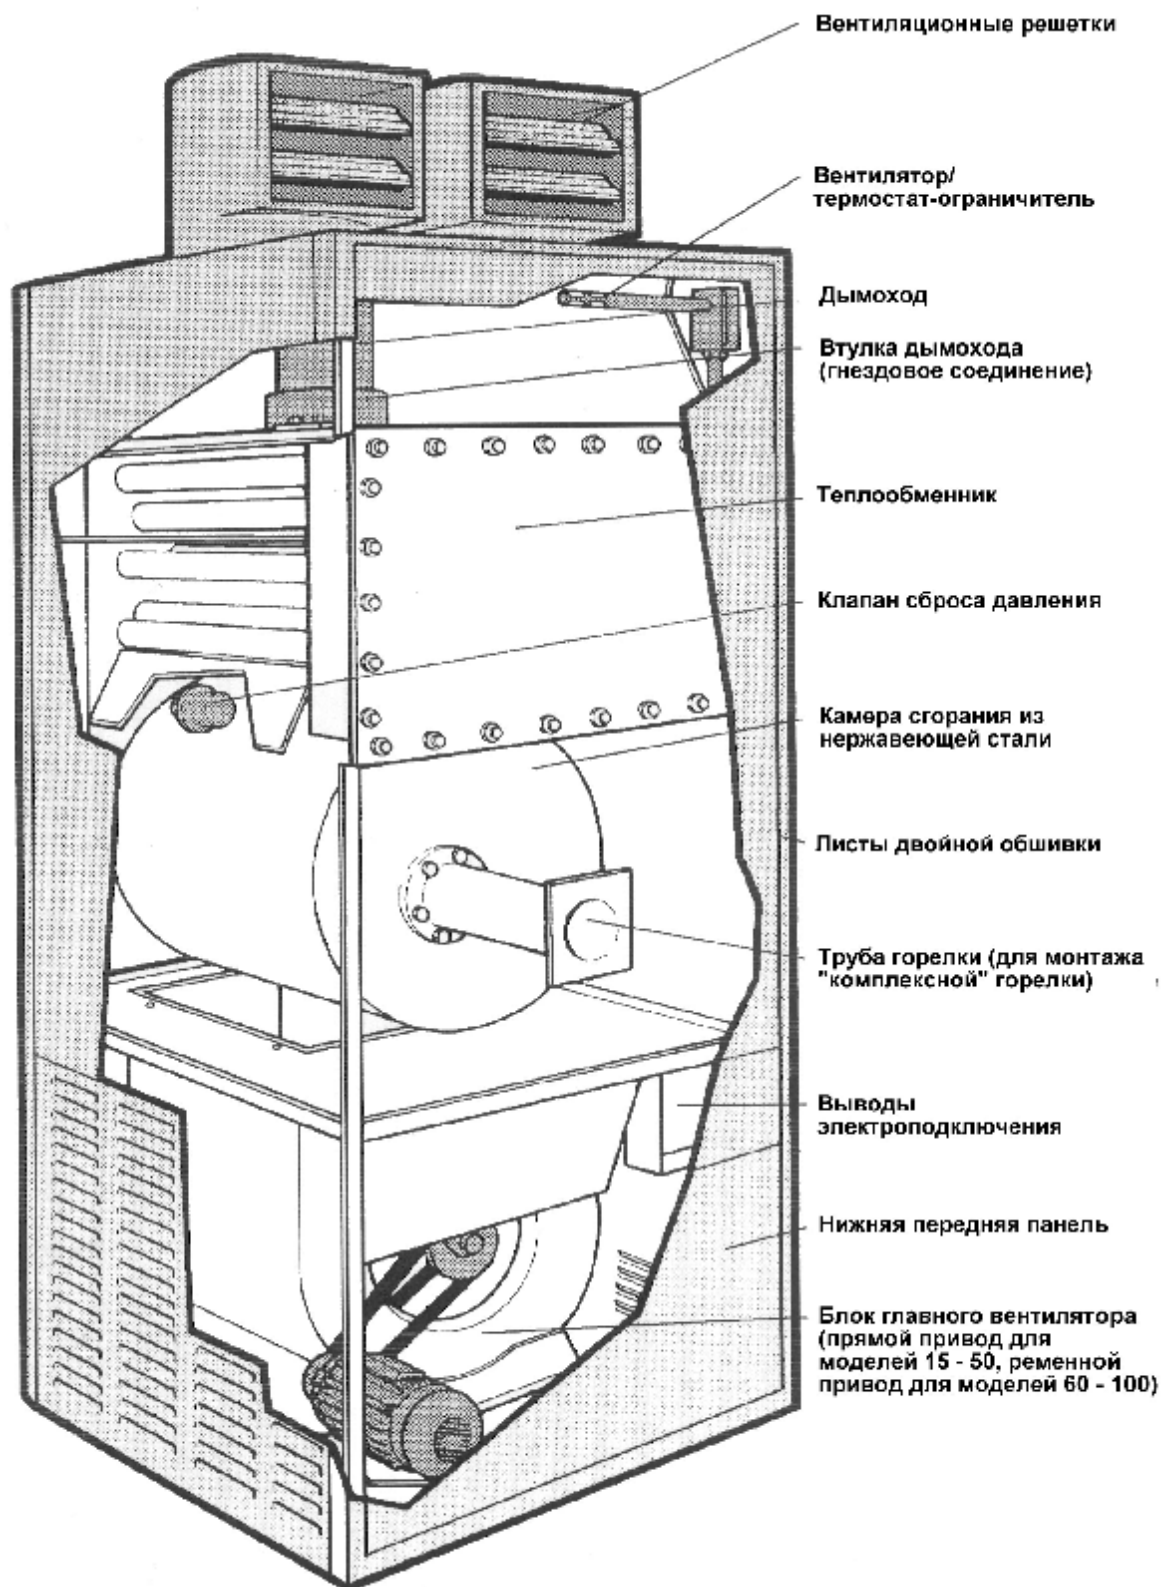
Стандартный шкаф-нагреватель «PGP»/«POP» – схема общего расположения
